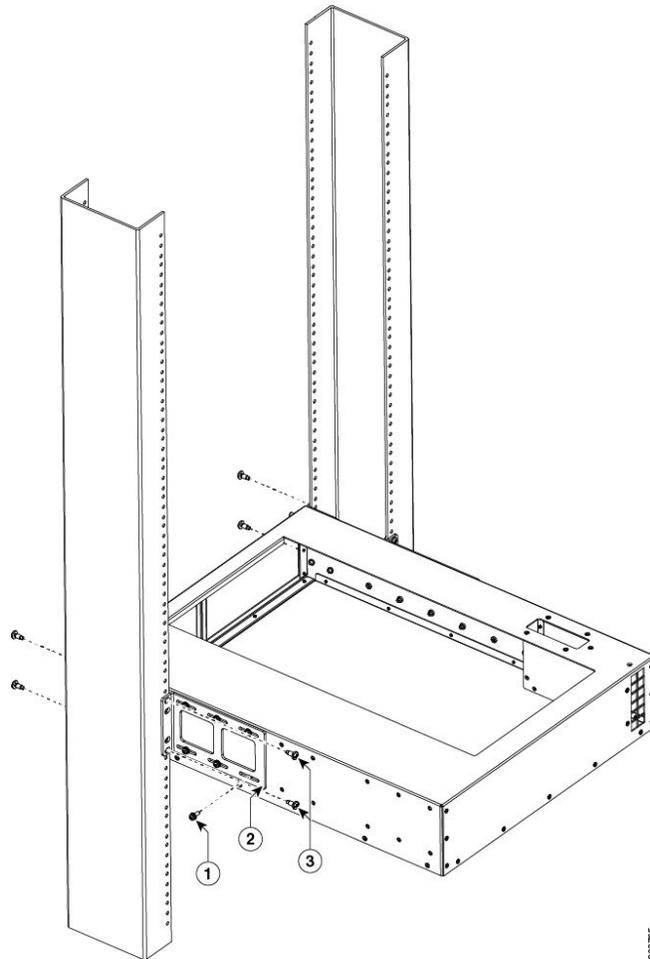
Cámara con soportes de montaje delanteros instalados previamente
